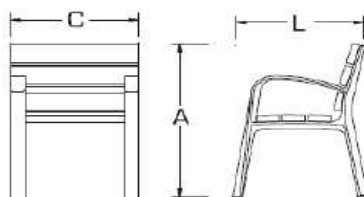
Croquis de Sillas Coimbra. (Fuente: <http://www.bricantel.pt/es/>)
